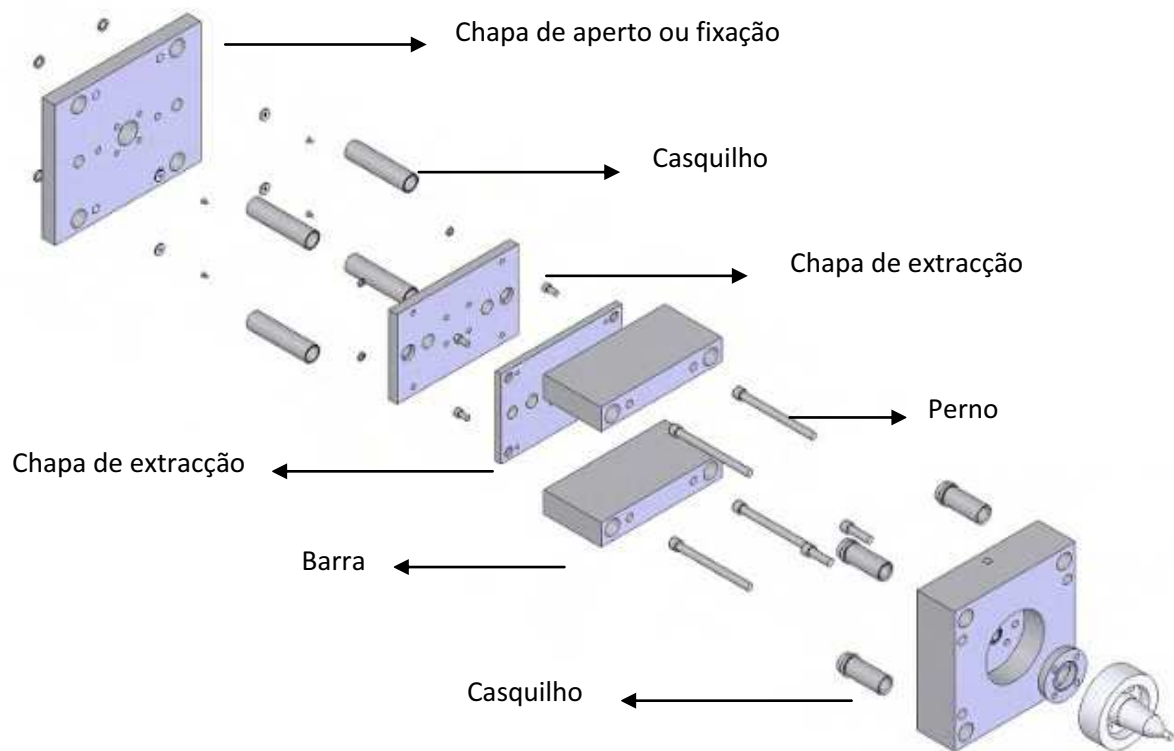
Desenho 3D dos componentes do molde - parte de extracção
